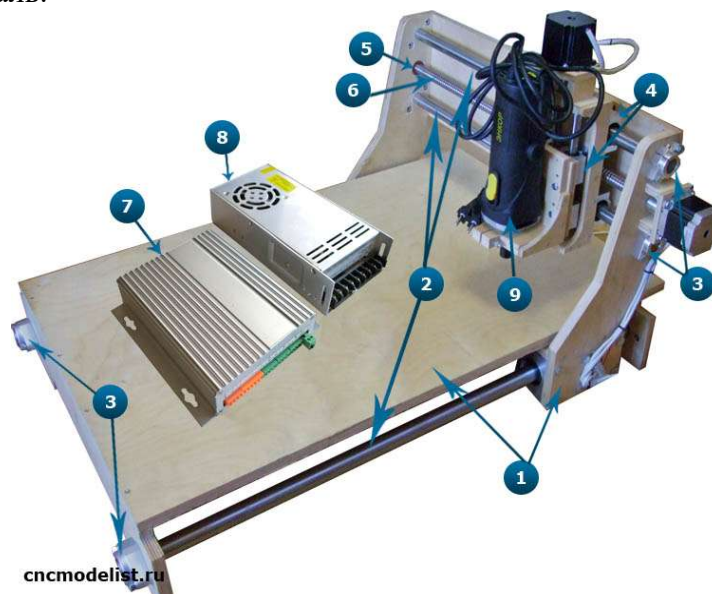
Фрезерный станок с подвижным порталом (портальный станок)
